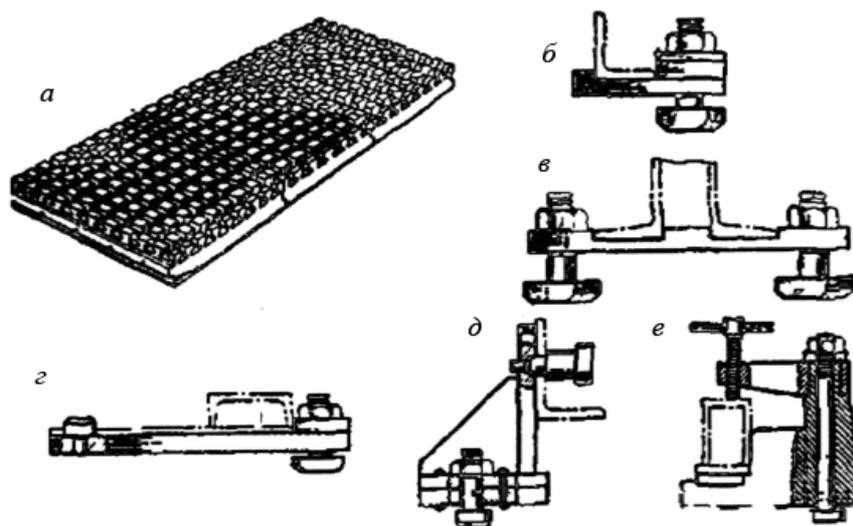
Элементы универсальных сварочных приспособлений:
